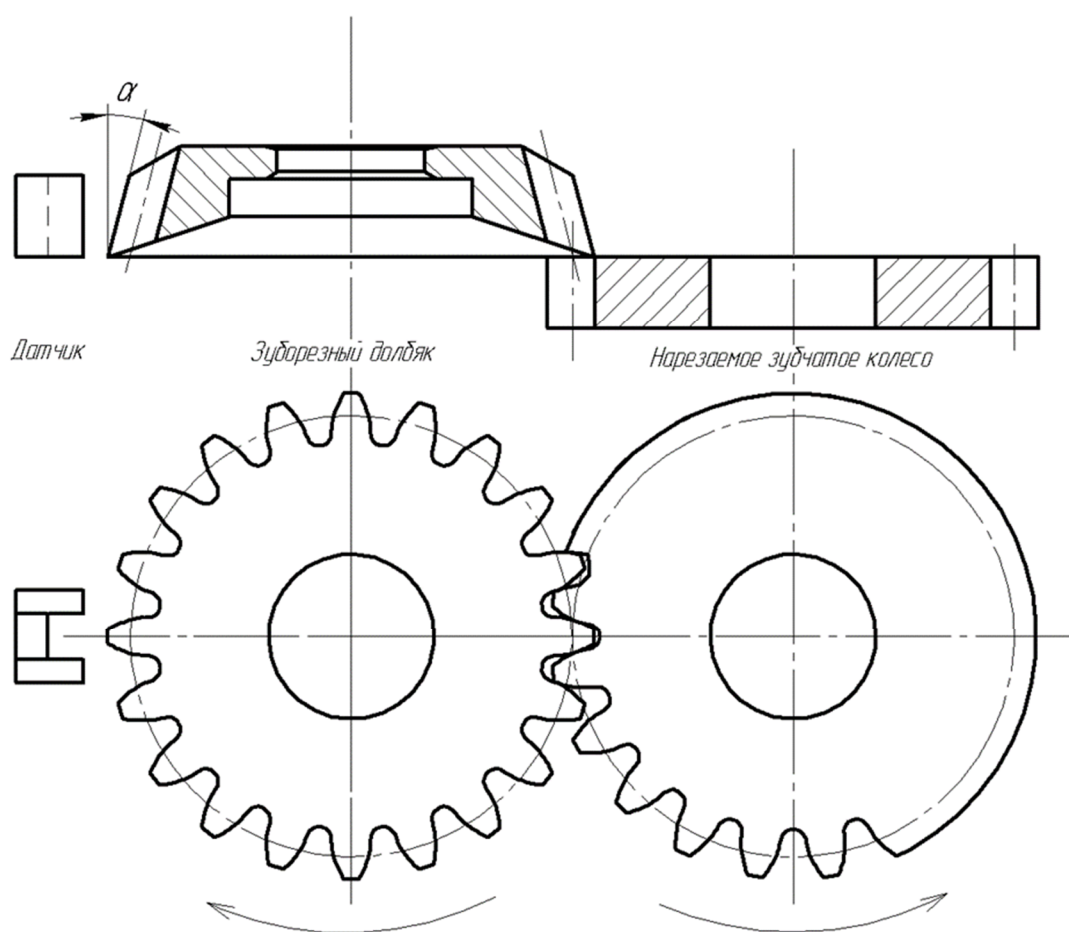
Схема установки магнитного датчика для контроля износа зуборезного долбяка в процессе нарезания зубчатого колеса
